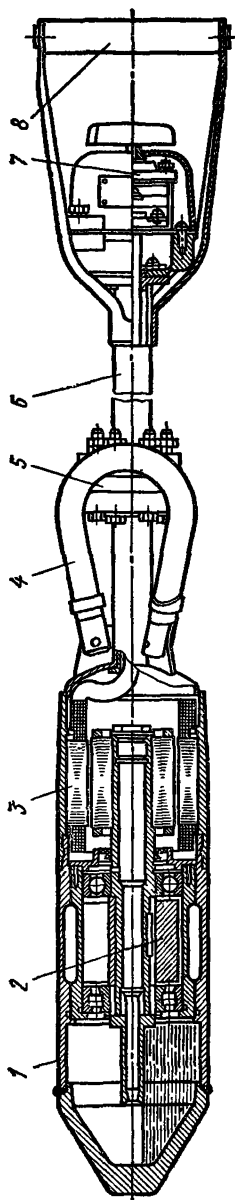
Ручной глубинный вибратор ИВ-59 со встроенным электродвигателем:
